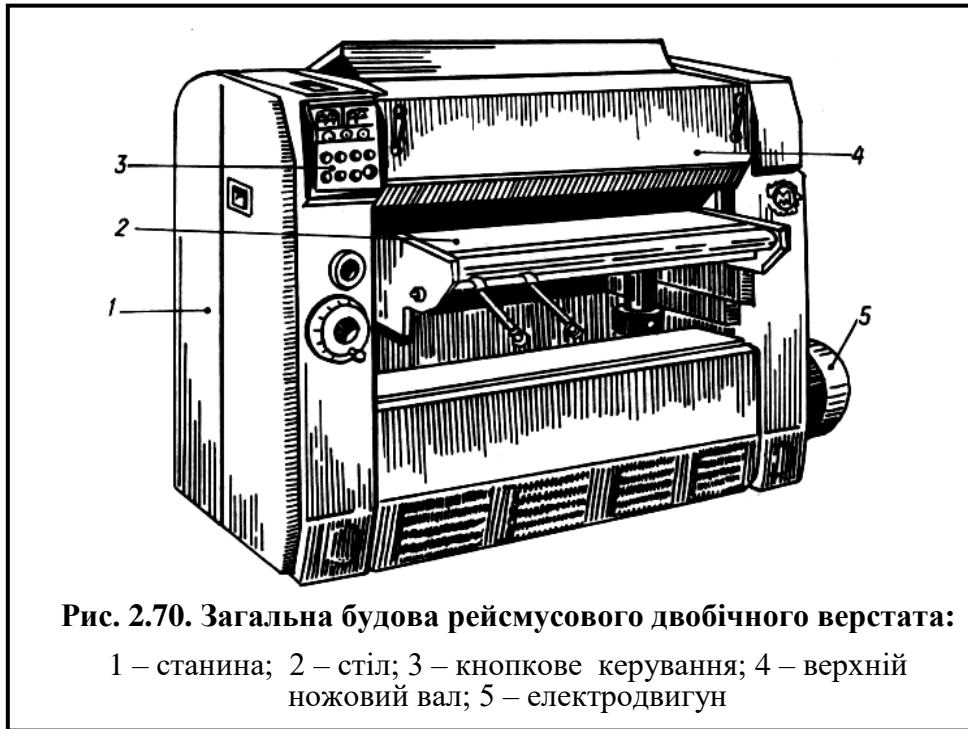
Загальна будова рейсмусового двобічного верстата:
